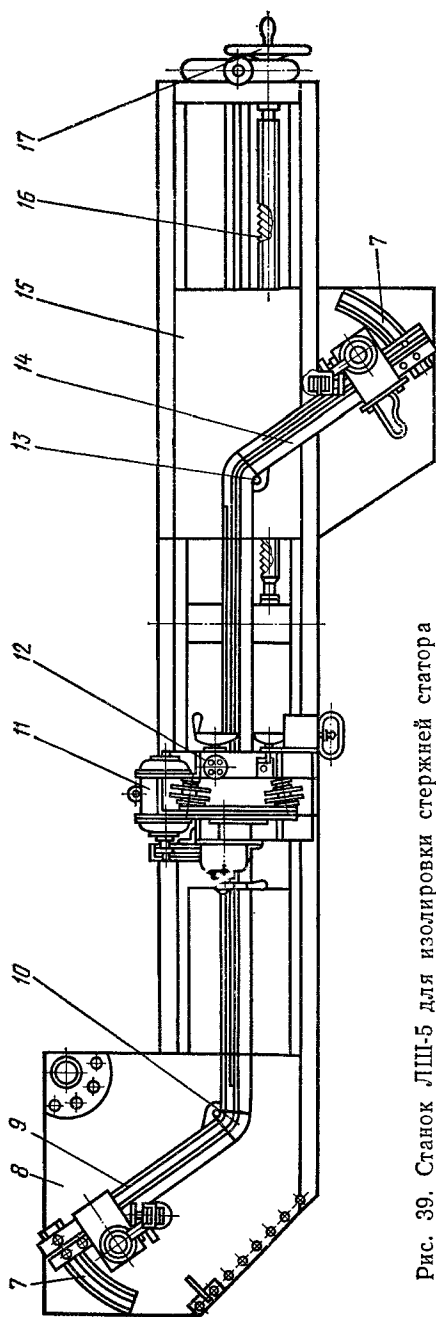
Станок ЛШ-5 для изолировки стержней статора
